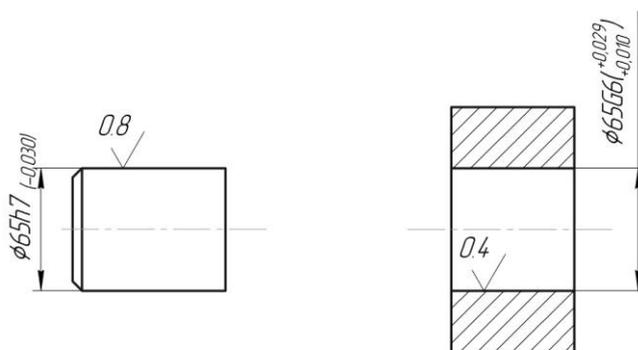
Ескізи деталей з'єднань  $\varnothing 65 \frac{G6}{h7}$
